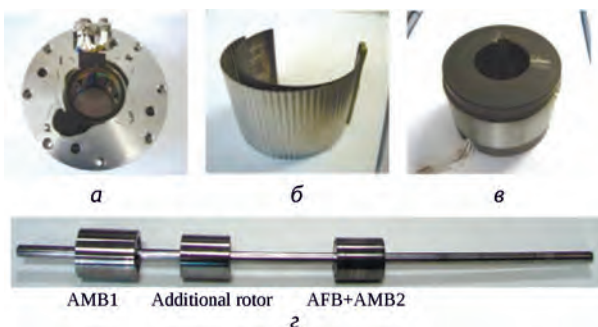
Ротор и подшипники испытательного стенда [46]: а – магнитный подшипник 1; б – лепестковый подшипник; в – магнитный подшипник 2; г – ротор
